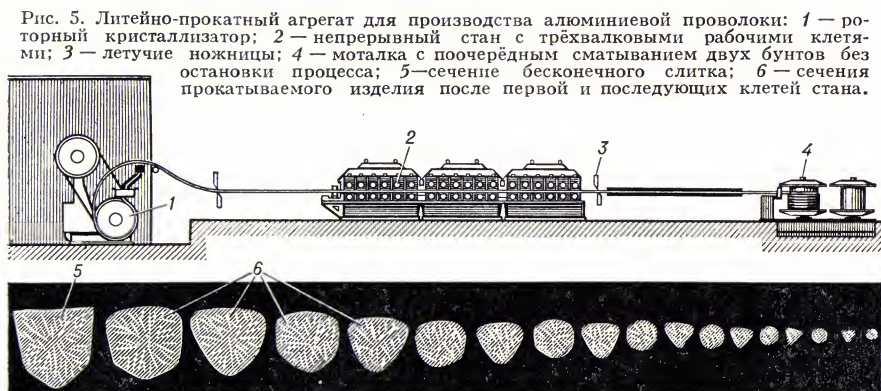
Литейно-прокатный агрегат для производства алюминиевой проволоки: 1 — роторный кристаллизатор; 2 — непрерывный стан с трёхвалковыми рабочими клетями; 3 — летучие ножницы; 4 — моталка с поочерёдным сматыванием двух бунтов без остановки процесса; 5 — сечение бесконечного слитка; 6 — сечения прокатываемого изделия после первой и последующих клетей стана.
